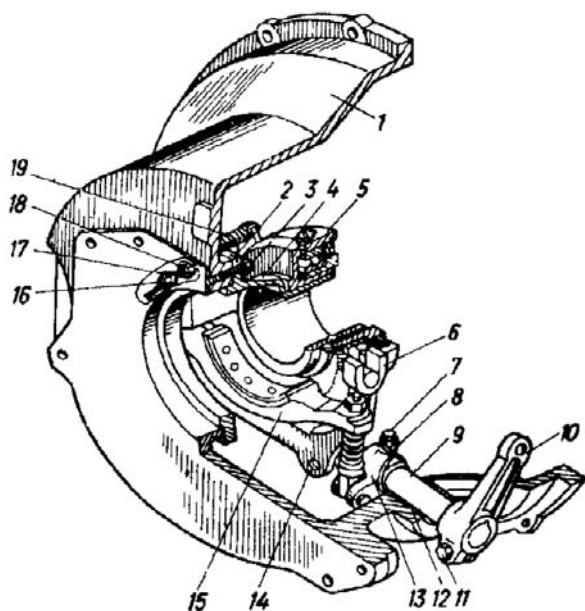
Сборка корпуса: 1 — корпус; 2 — шайба; 3, 7, 11, 14, 16, 18 — болт; 4 — стакан; 5 — подшипник выжимной; 6 — вилка; 8, 17 — проволока; 9 — валик; 10 — рычаг; 12 — втулка; 13 — серьга тормозка; 15 — колодка; 19 — пружина
